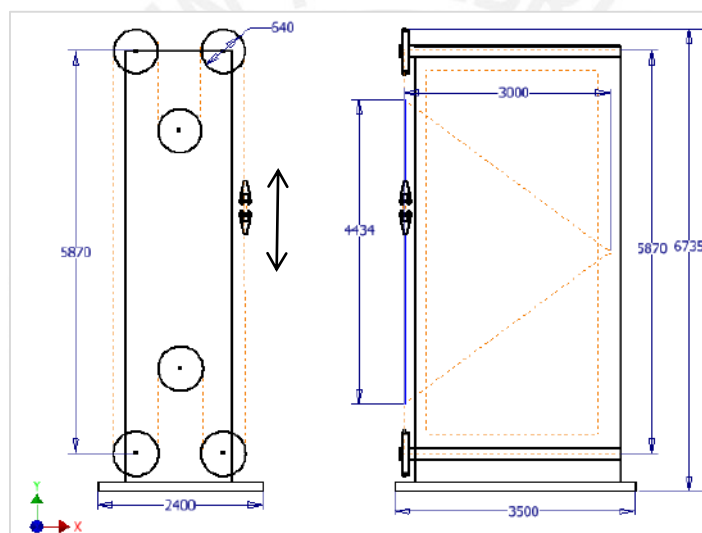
Esquema dimensional y carrera de la máquina de ensayos.
